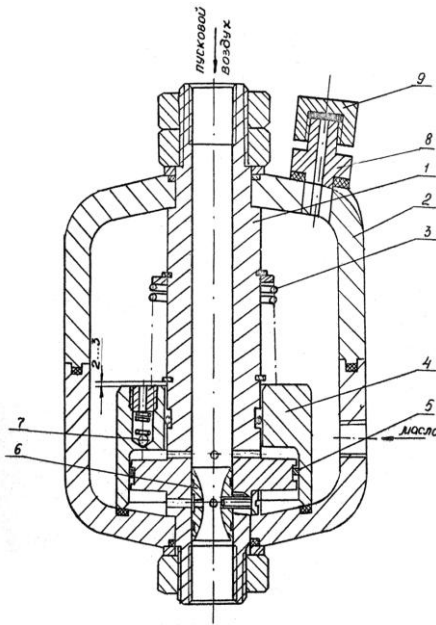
Устройство масловпрыска: 1 – стержень; 2 – резервуар для масла; 3 – пружина; 4 – поршень; 5 – уплотнительные кольца; 6 – диффузор; 7 – клапан; 8 – штуцер; 9 – заглушка
